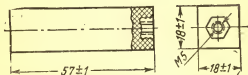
Габаритный чертеж столбов Д1004, Д1005А.
